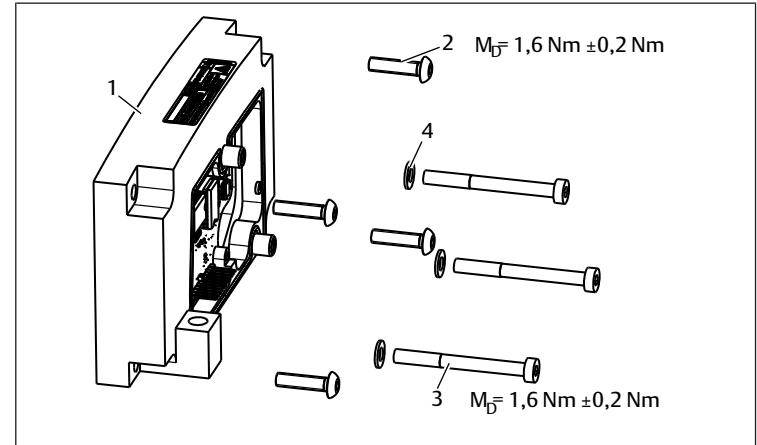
Vue d'ensemble du module adaptateur AES-Serie 500
